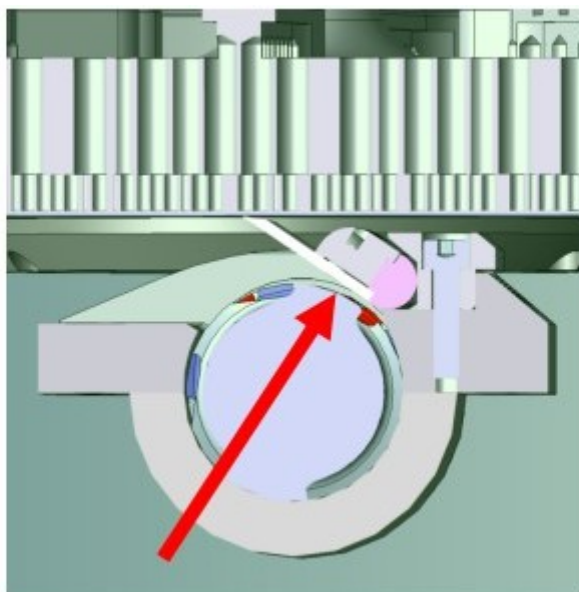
CAD-Schnittzeichnung durch die angegriffenen Ausführungsformen
